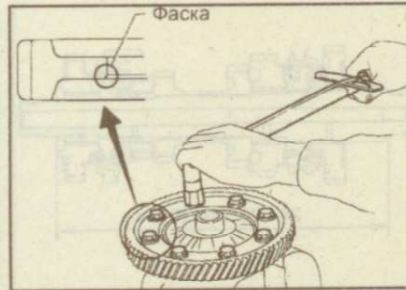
Выворачивание болта крепления ведомой шестерни главной передачи к коробке дифференциала
